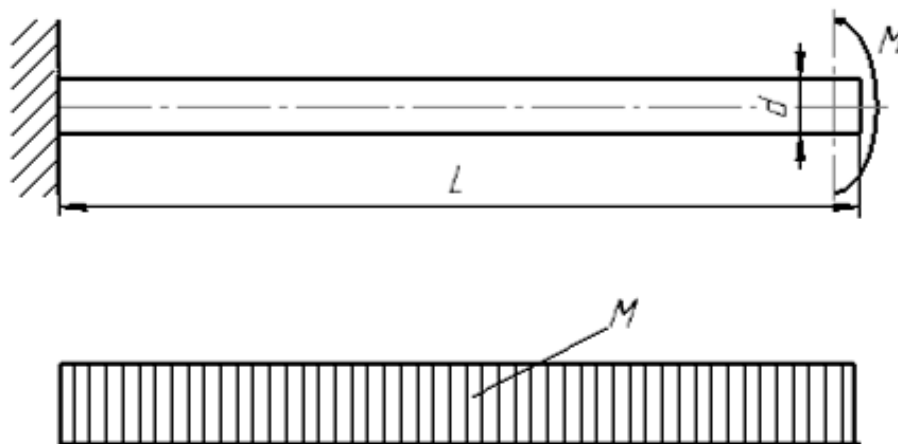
Схема деформации длинномерной цилиндрической детали при ее вибромеханической стабилизации
